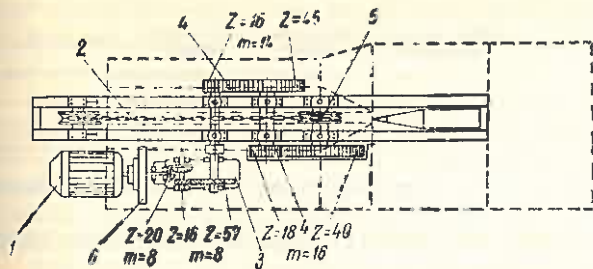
Schema cinematică a despicătorului indigen DL-8.
